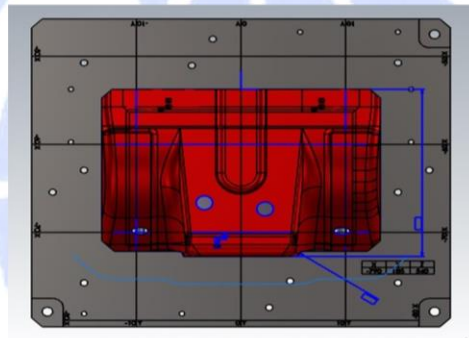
Autocad 2D Floor Shifter CF Tampak Depan
